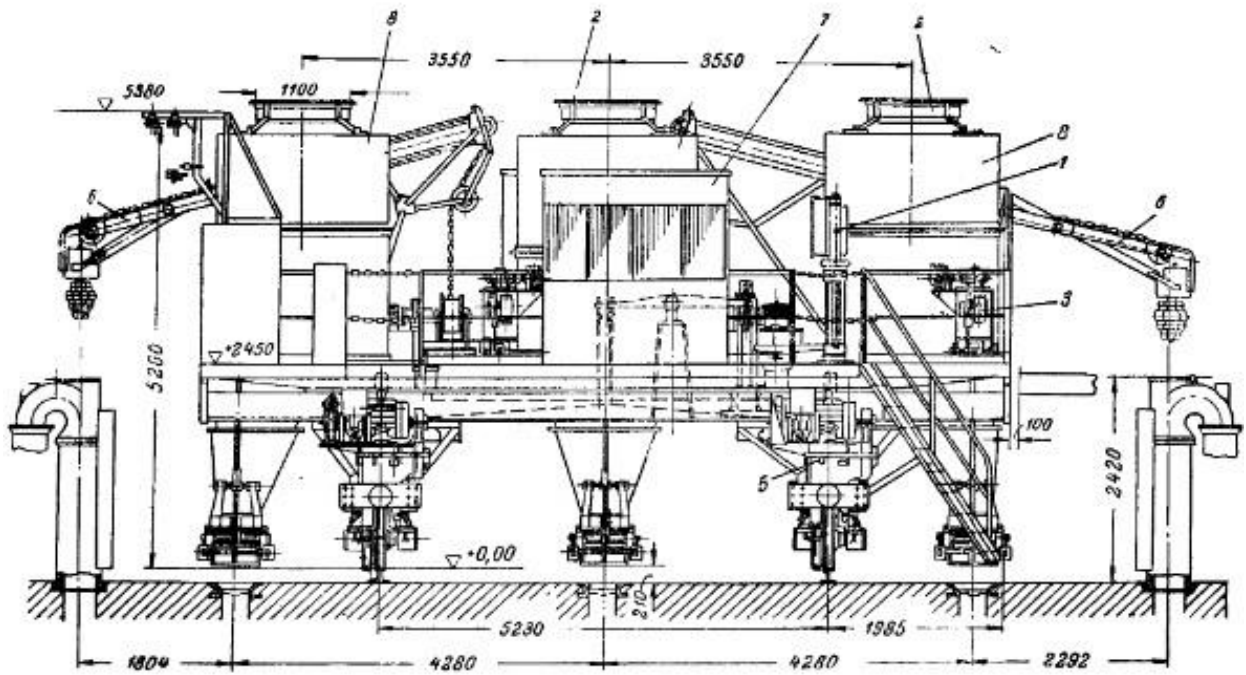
Трьохбункерний вуглезавантажувальний вагон конструкції конструкторського бюро Главмашмета. Вид спереду.
